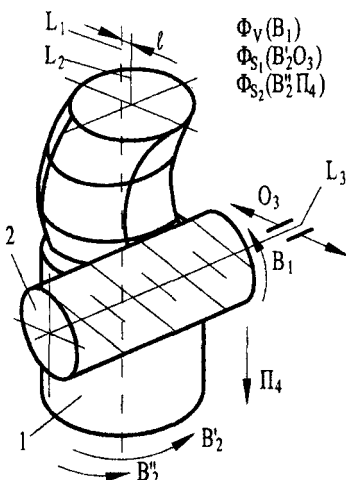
Схема обработки круговой винтовой поверхности цилиндрической фрезой
